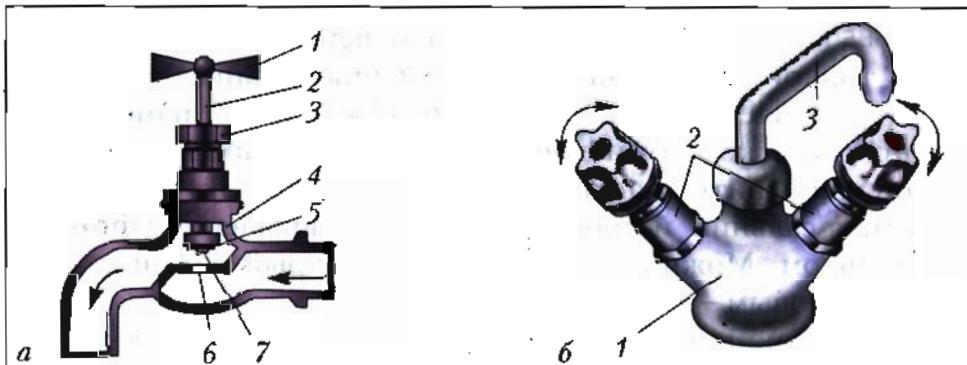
Водопроводное оборудование: а — водопроводный кран:
